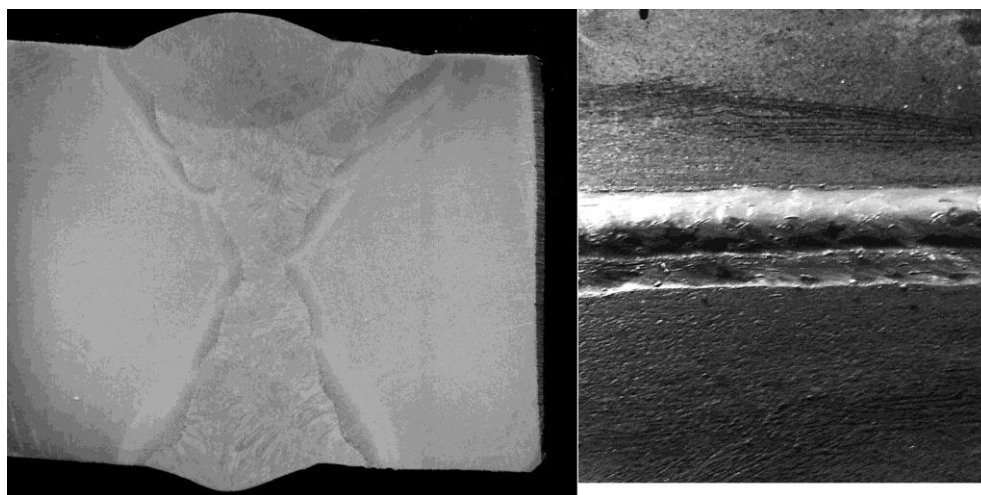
Macrofotografia da junta de teste e foto da solda, soldada com o arame maciço AWS ER80S-G.
